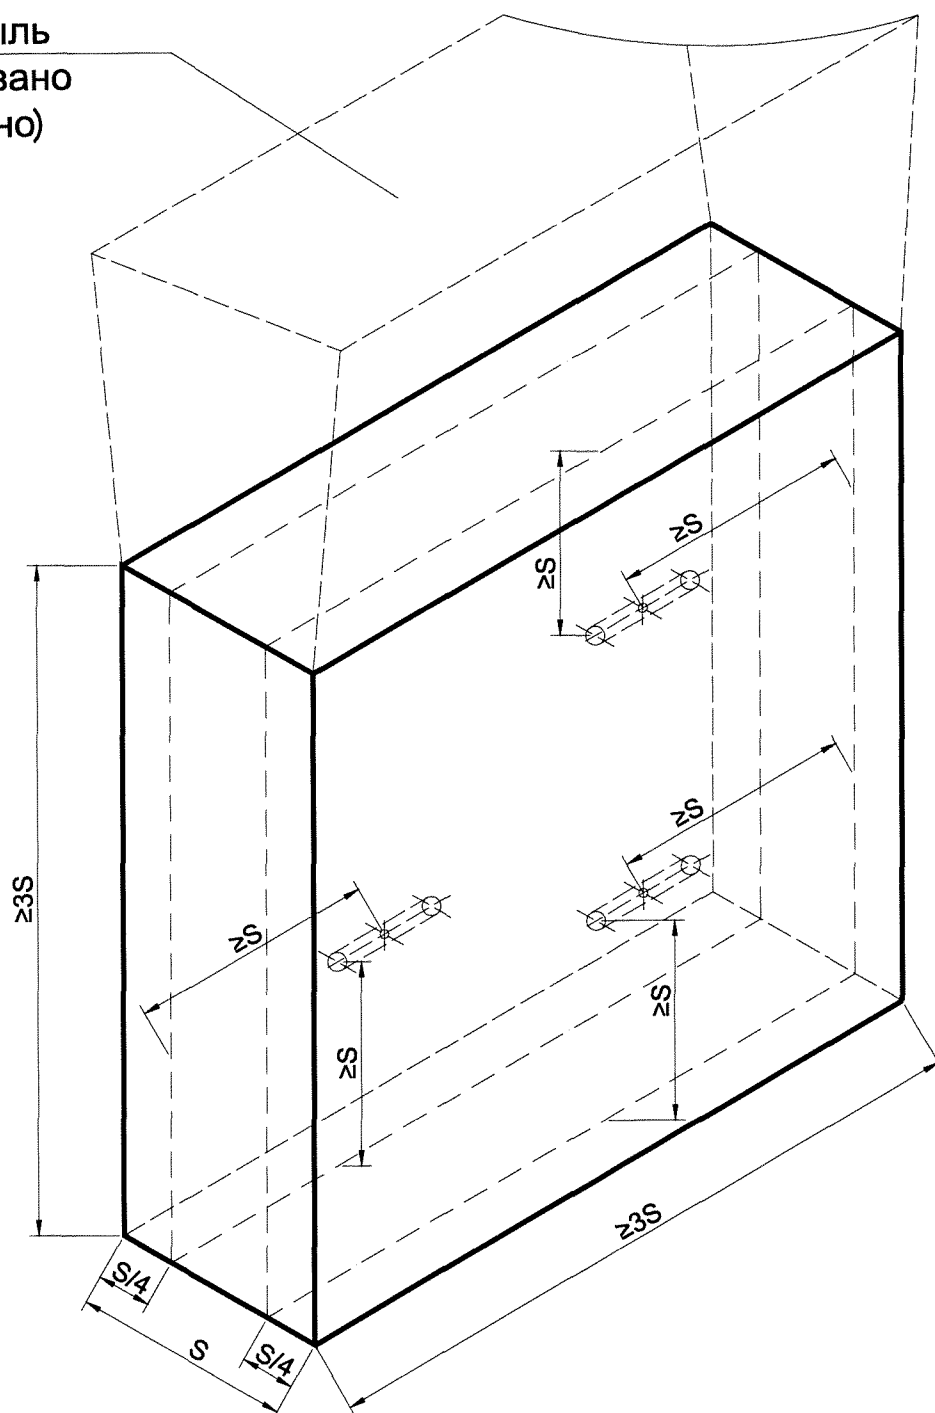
Схема отбора образцов для испытаний механических свойств из отдельно отлитой пробы
